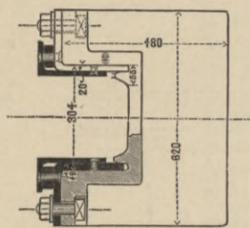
Grundriss und wagenrechter Schnitt.
